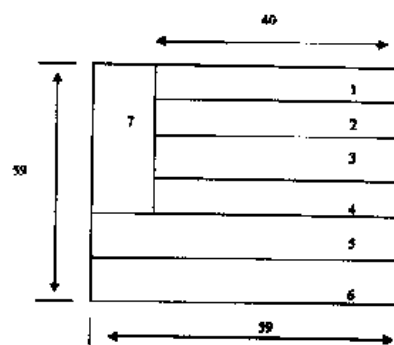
Схема разделки темплета. 1-4 – заготовки под образцы для механических испытаний на растяжение 5, 6 – заготовки под образцы для испытаний на ударный изгиб 7 – заготовка под образцы для металлографических и структурных исследований.
